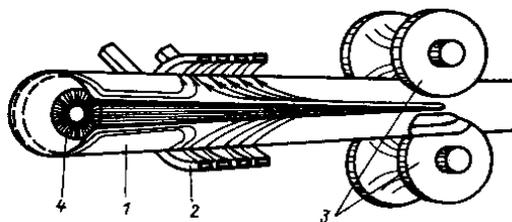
Схема индуктивного токоподвода при непрерывной высокочастотной стыковой сварке:
